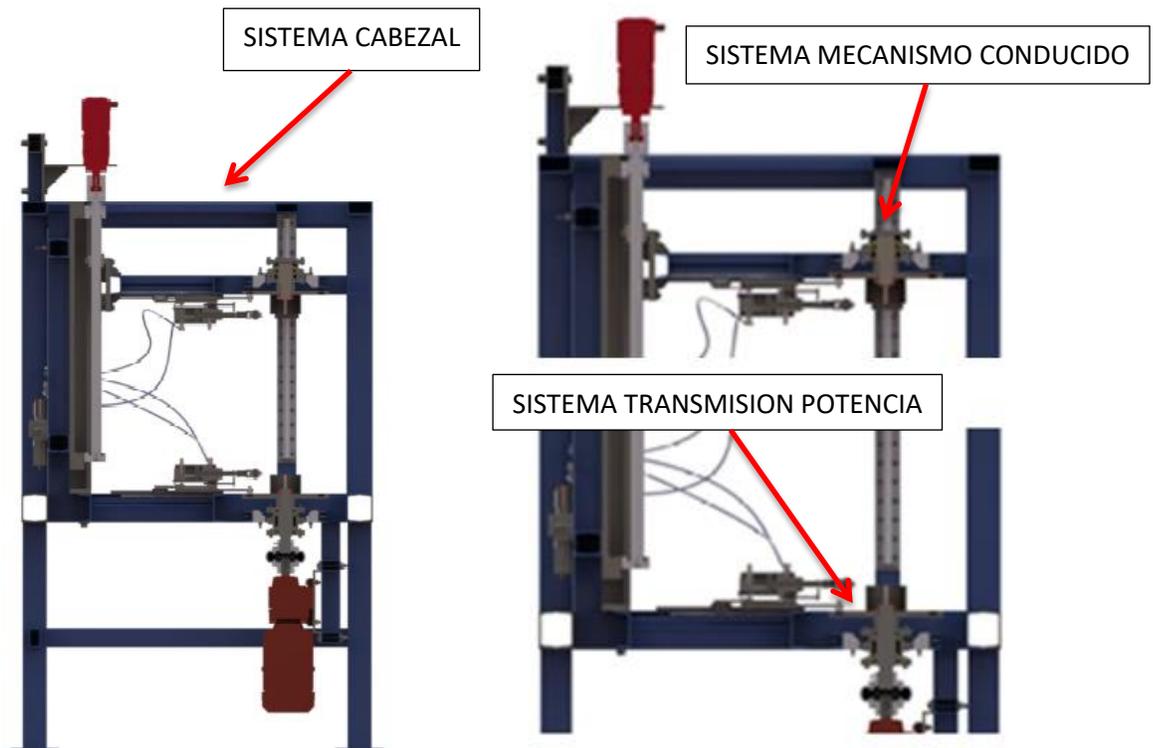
Vista en corte de la maquina engrafadora sin el conjunto carcasa
